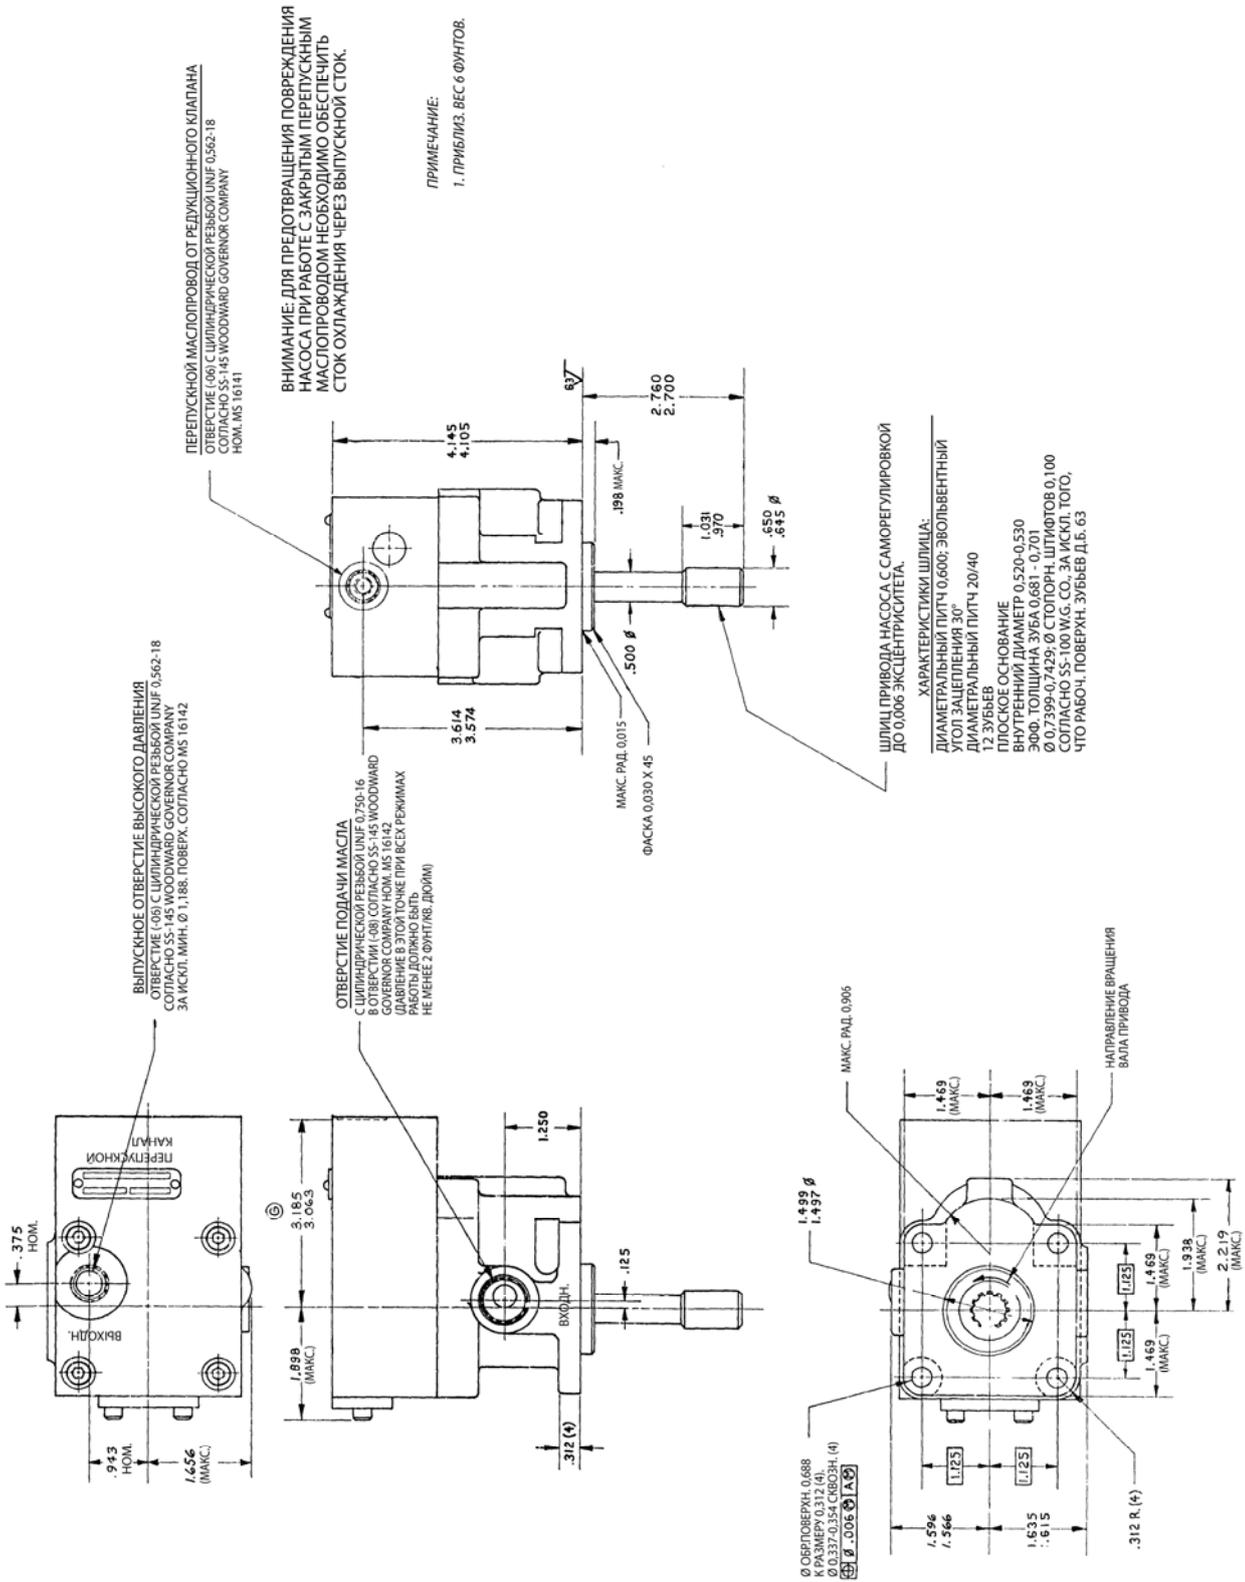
Габаритный чертеж (8580-065, -080, -083, -085, -086; 9902-072, -092)
